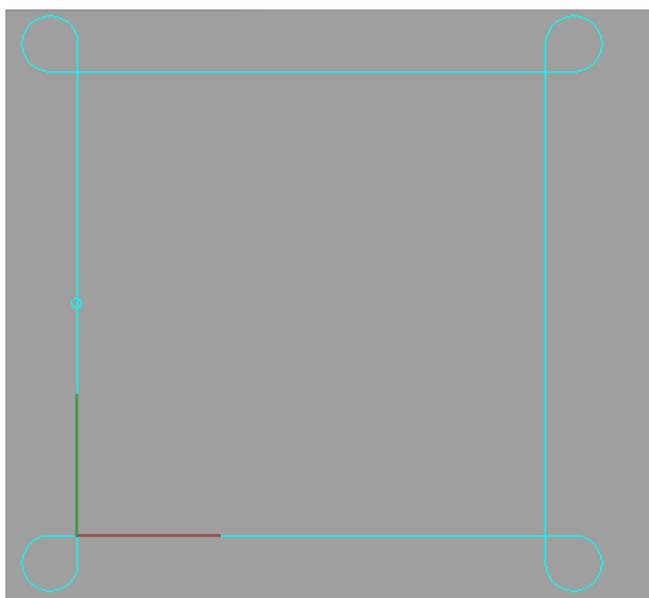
Схема обработки заготовки с помощью инструмента «Авторасстановка петель»
